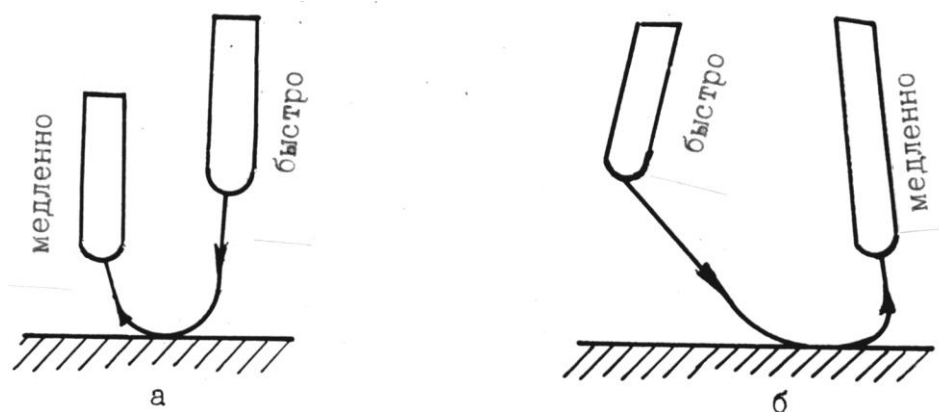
Способы зажигания сварочной дуги:
